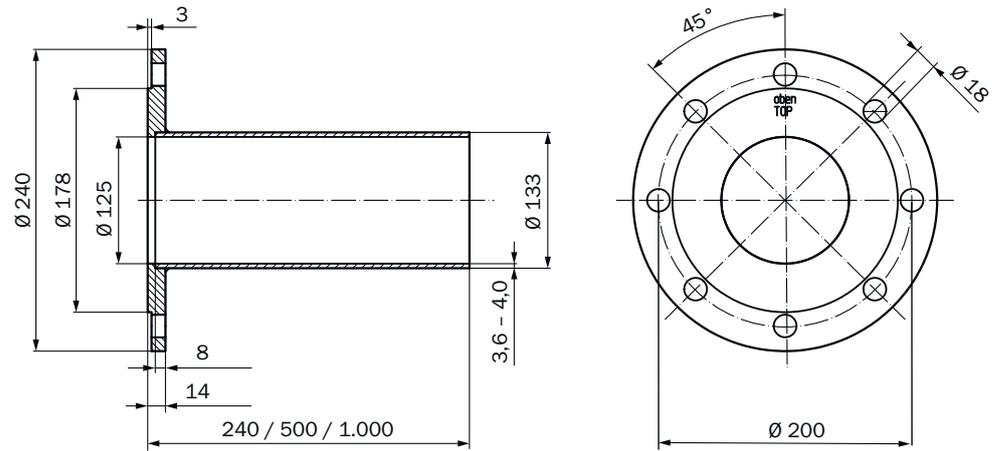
Flansch mit Rohr DN125 (Maße in mm)
